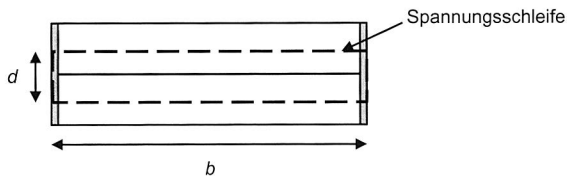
Schweißpaketiertes Paket mit zwei Blechen, Maße der Spannungsschleife
